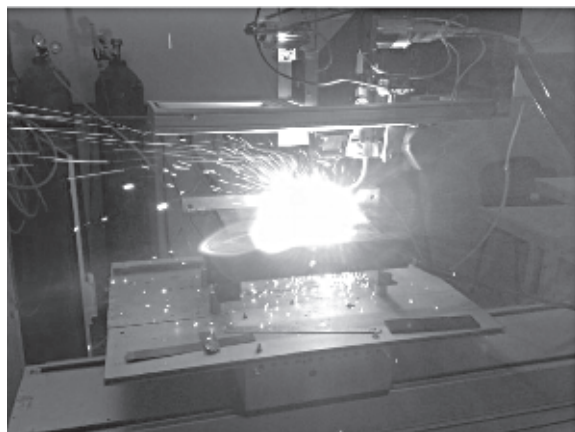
Процесс лазерно-дуговой сварки
